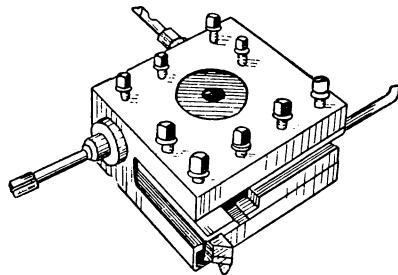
Поворотный резцедержатель с гнездами для установки сверл, зенкеров и разверток.
